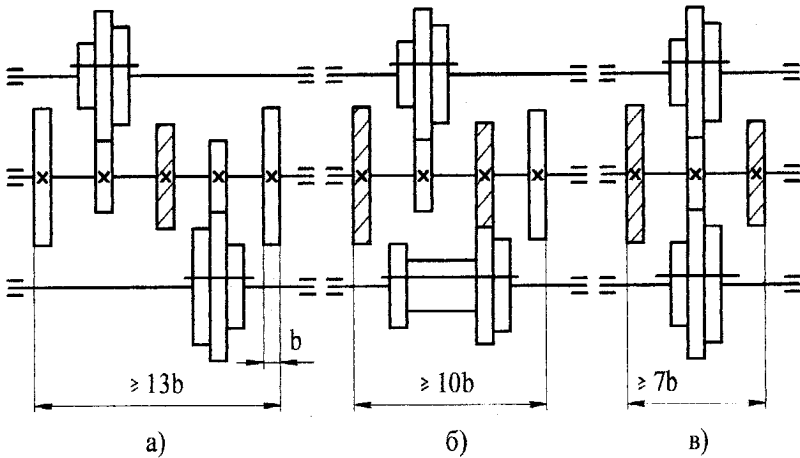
Механізми із зв'язаними зубчастими колесами.
